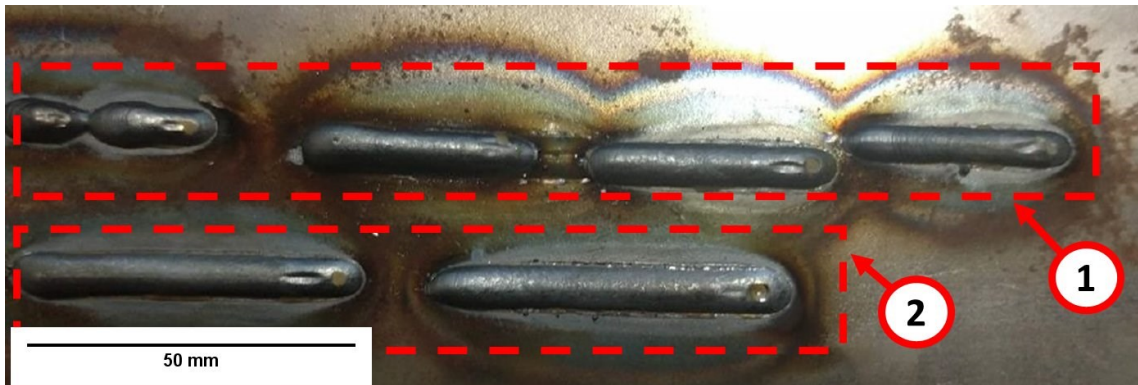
Soldagem cordão sobre chapa GMAW (Próprio autor)
